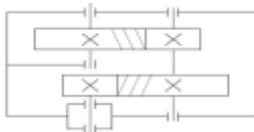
Кинематическая схема двухступенчатого соосного цилиндрического редуктора
